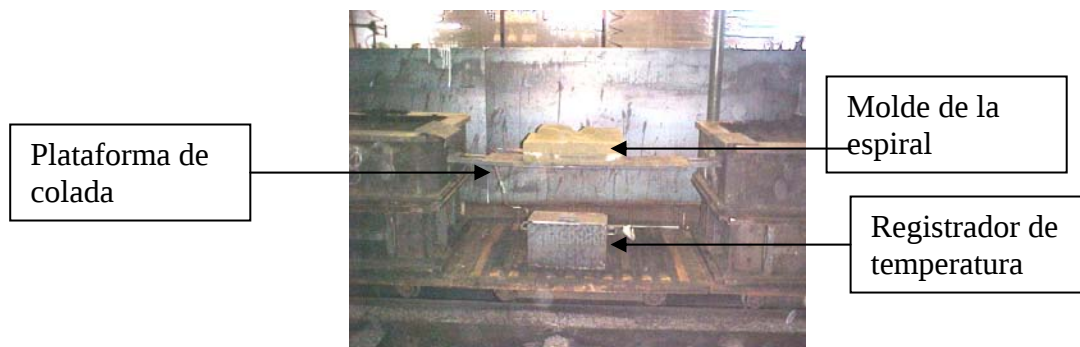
Montaje del molde de las espirales en la línea de colada.
